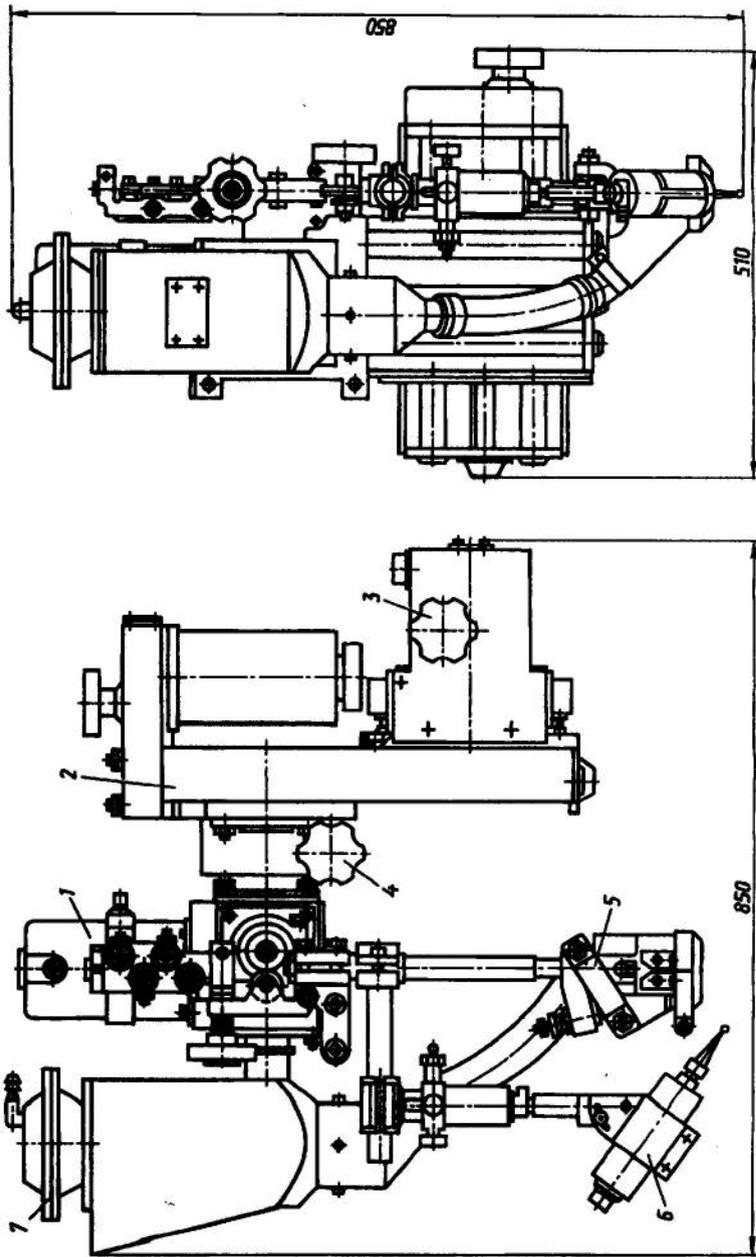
Автомат АД-202 для дугового зварювання:
